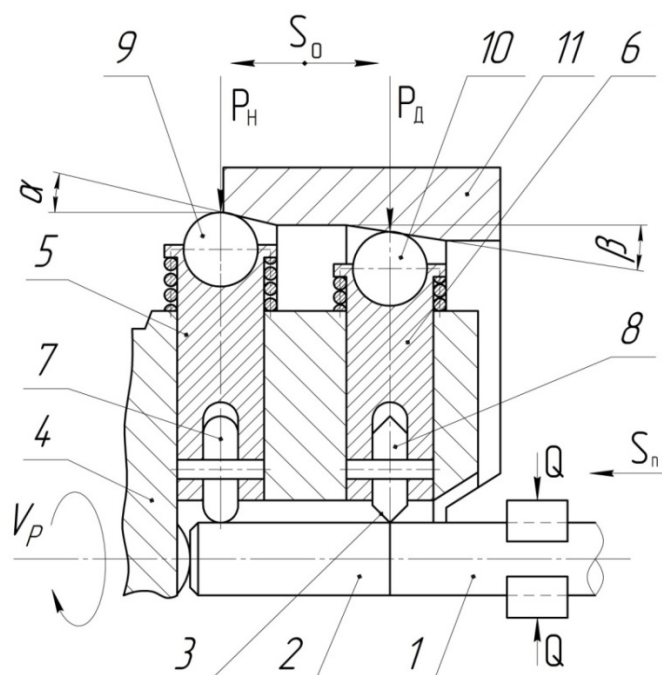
Схема устройства для разделения прутка на мерные заготовки
